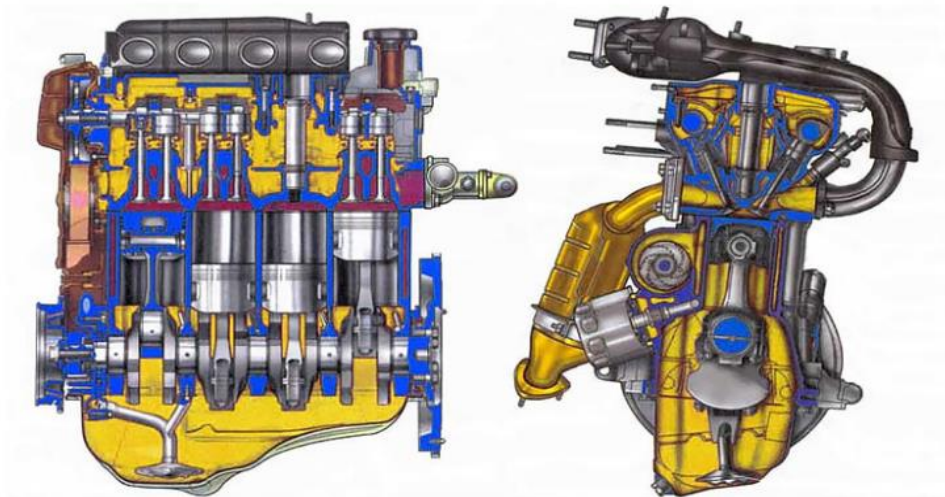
общий вид двигателя «ВАЗ – 21126»
